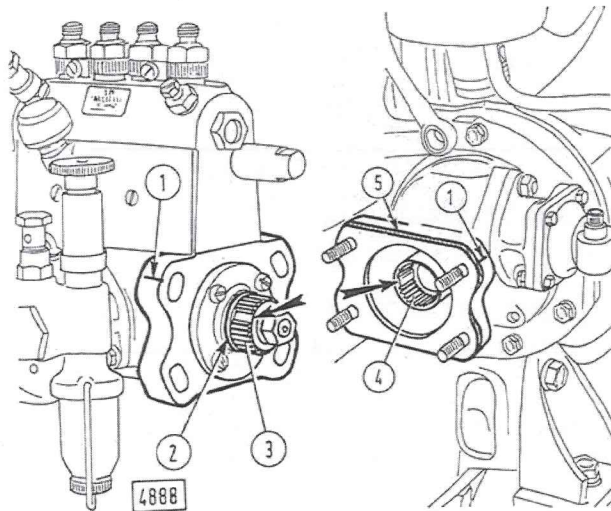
Montaggio della pompa iniezione sul motore.
